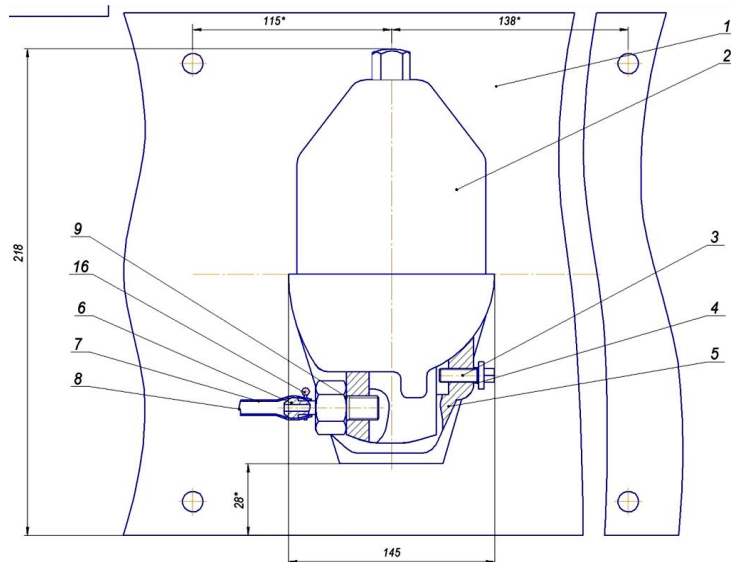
Розміщення фільтра на корпусі коробки передач: 1 – корпус; 2 – фільтр; 3 – пробка; 4 – прокладка; 5 – кришка; 6 – штуцер; 7 – арматура; 8 – шланг; 9 – прокладка.
